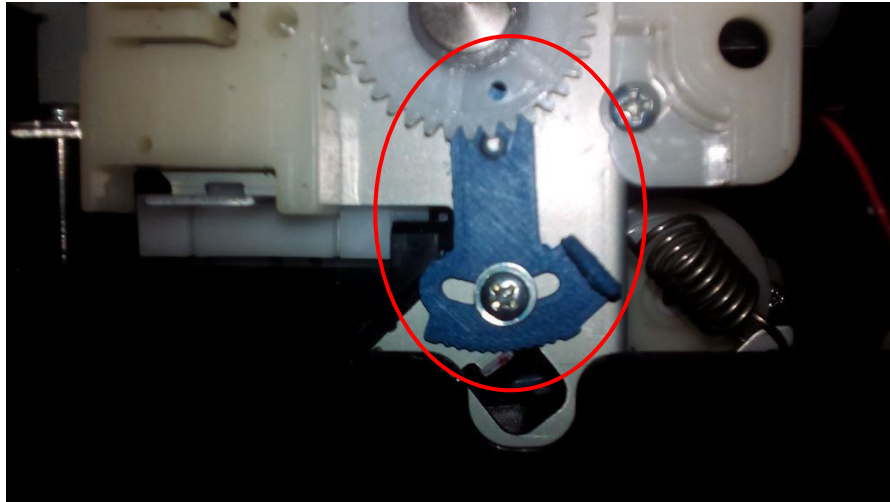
Fotografía del soporte izquierdo instalado en la impresora
